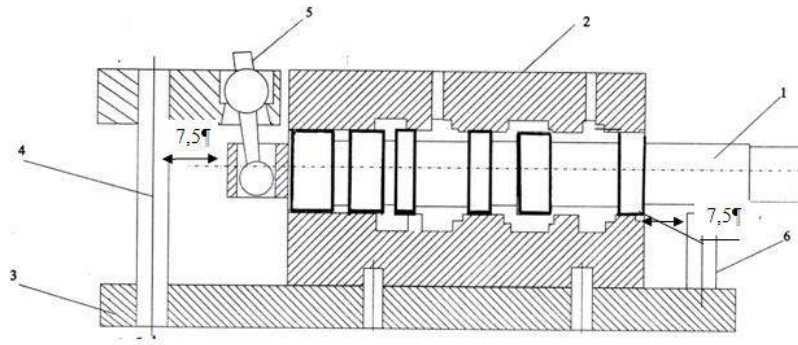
Схема з'єднання золотника з важелем пристосування для безабразивної орієнтованої притирки золотникових пар: 1 – золотник; 2 – корпус гідророзподільника; 3 – основа; 4, 6 – обмежувачі; 5 – знімний важіль.
